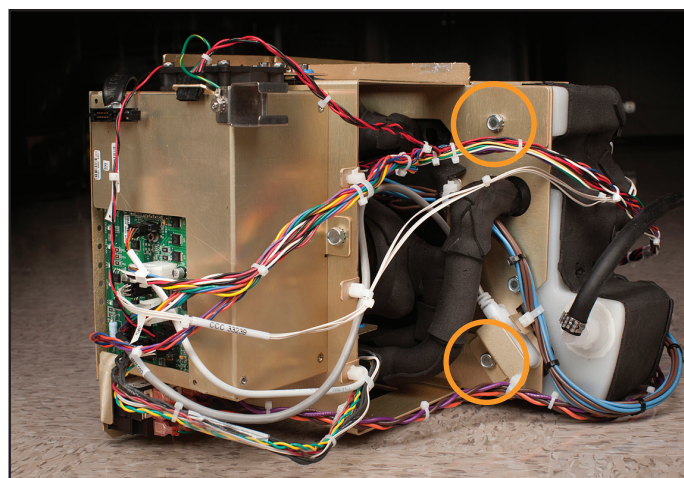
Interne komponenter (sett bakfra); sirkler indikerer bolter som skal fjernes (trinn 1)
